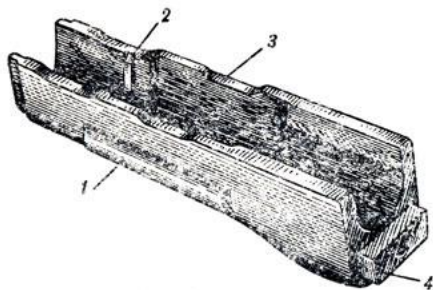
Цевье: 1 - упор для пальцев; 2 - металлическая прокладка; 3 - вырез; 4 - выступ
